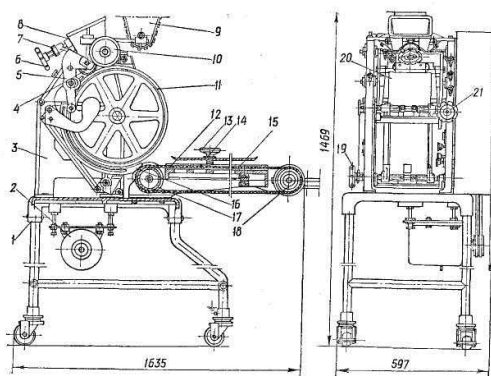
Тістозаковувальна машина МЗЛ-51: 1 – станина; 2 – привід машини; 3 – боковини; 4, 10 – розкочувальні валки; 5 – завивальний пристрій; 6 – регулятор товщини розкочування; 7 – стопорна гайка; 8 – прийомна лійка; 9 – борошнопосипач; 11 – заковуючий барабан; 12 – стрічковий конвеєр; 13 – регулятор прижимної плити; 14 – притискна плита (подовжувач); 15 – стіл; 16 – торцеві обмежувачі довжини заготовки; 17 – привідний барабан; 18 – натяжний барабан; 19 – регулятор довжини заготовки; 20 – формуючий кожух; 21 –
